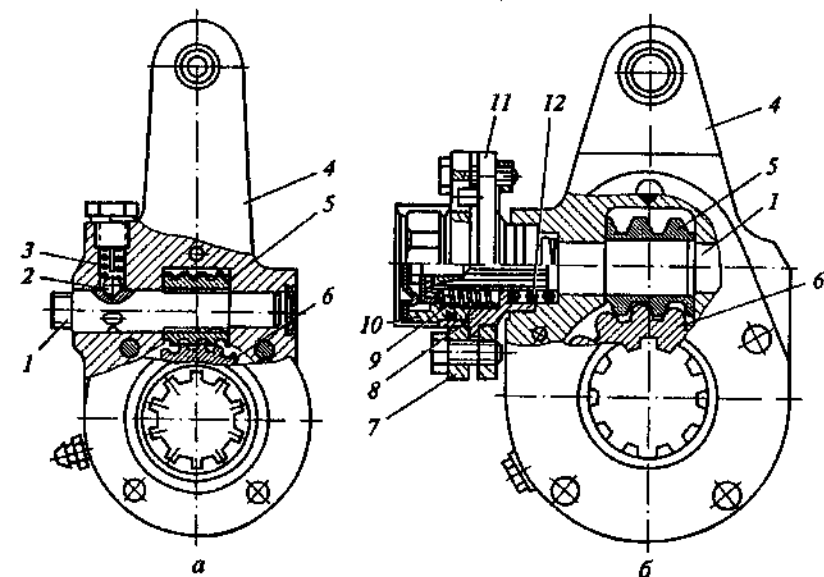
Регулировочные рычаги колесных тормозных механизмов с ручным (а) и автоматическим (б) регулированием: 1 — ось; 2 — фиксатор; 3, 9 и 12 — пружины; 4 и 8 — корпуса; 5 — червяк; 6 — шестерня; 7 — скоба; 10 — гайка; 11 — установочное кольцо
